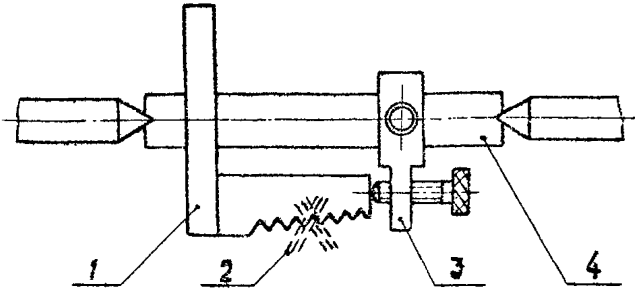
Приспособление для установки отливки в центрах микроскопа
